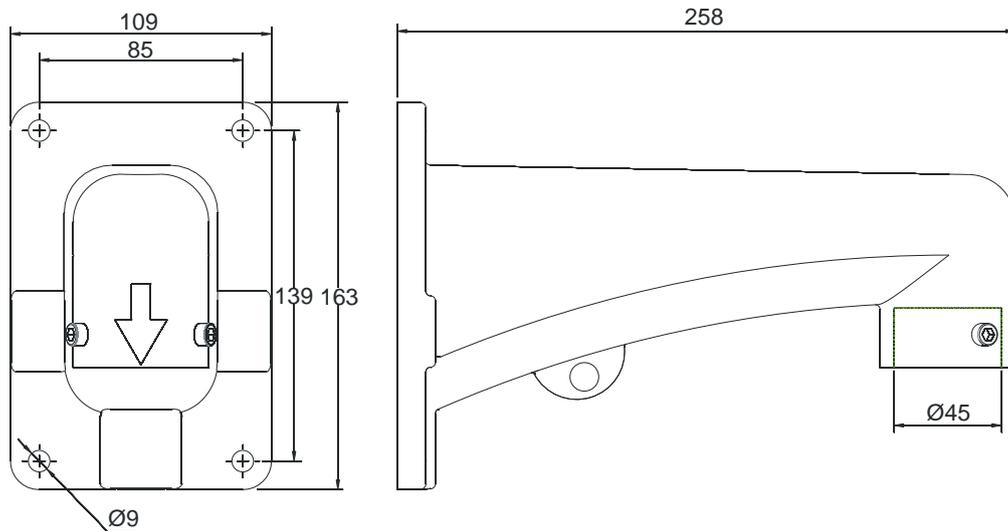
Bild mit den Abmessungen der an der Wand montierten Installationshalterung
